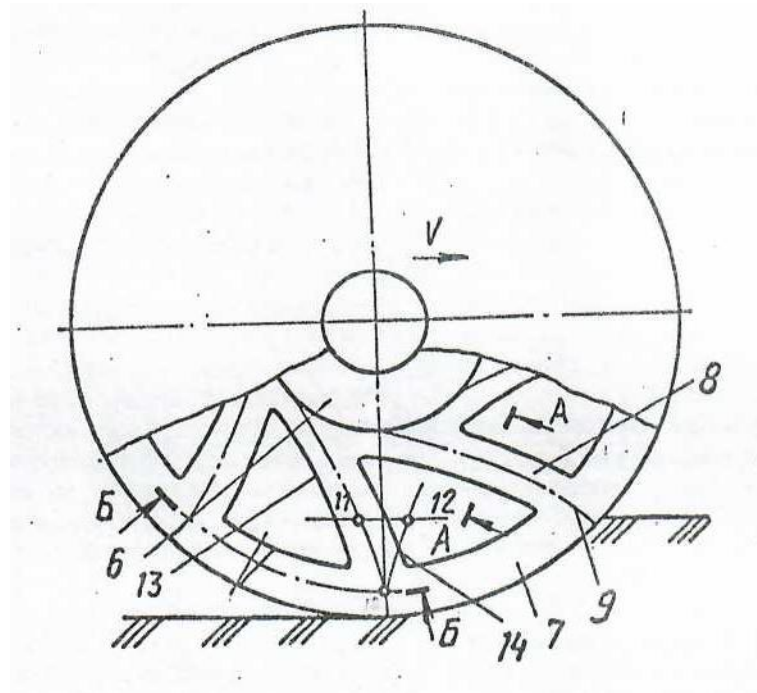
Визначення форми робочої поверхні спиці пасивного диска
